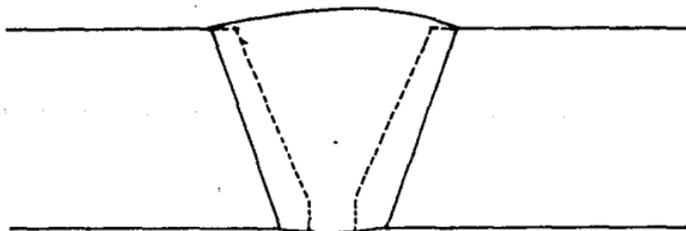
Soldadura con Bisel Sencillo en V
